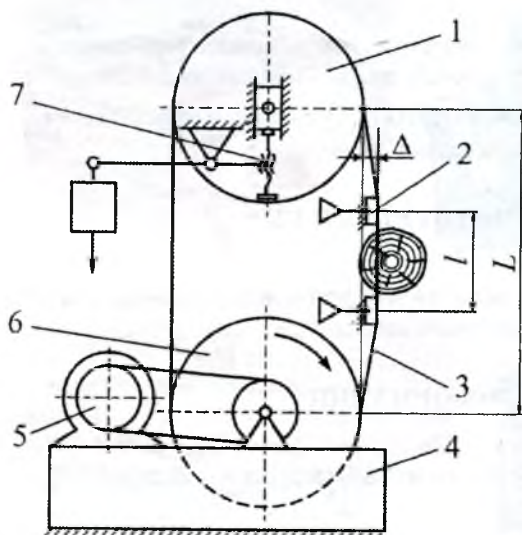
Схема устройства ленточнопильного станка с отжимными аэростатическими направляющими:
